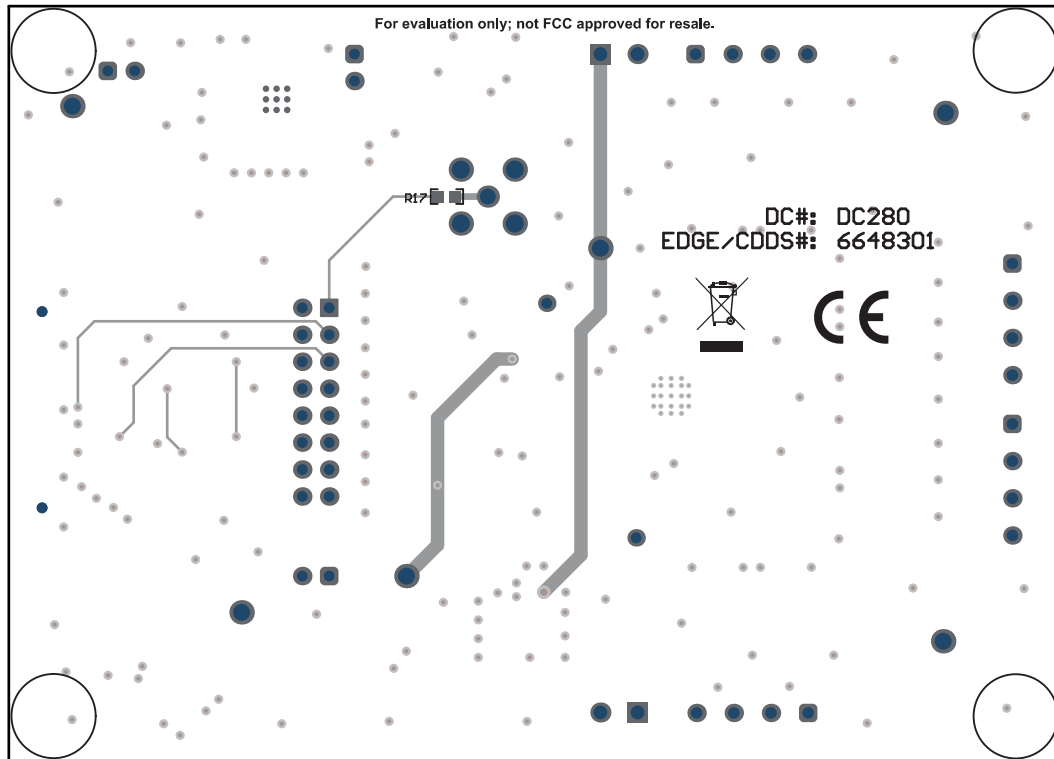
ADS125P08 EVM PCB 布局 — 底层
